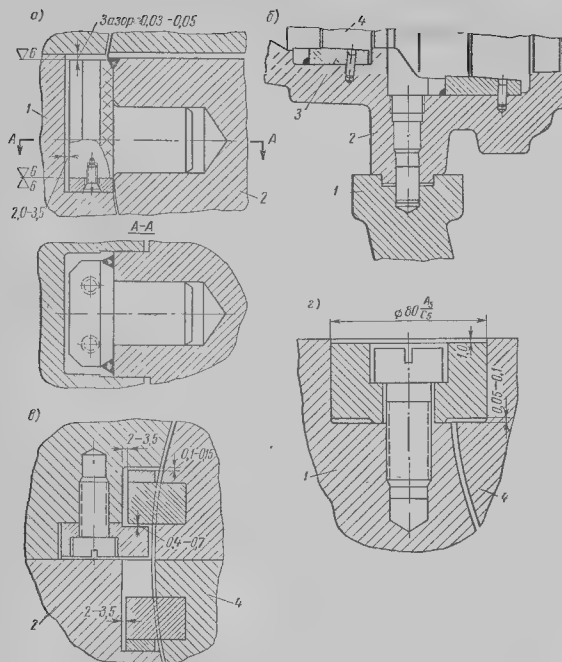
Конструкция крепления обойм и диафрагм в цилиндре турбины К-200-130:
